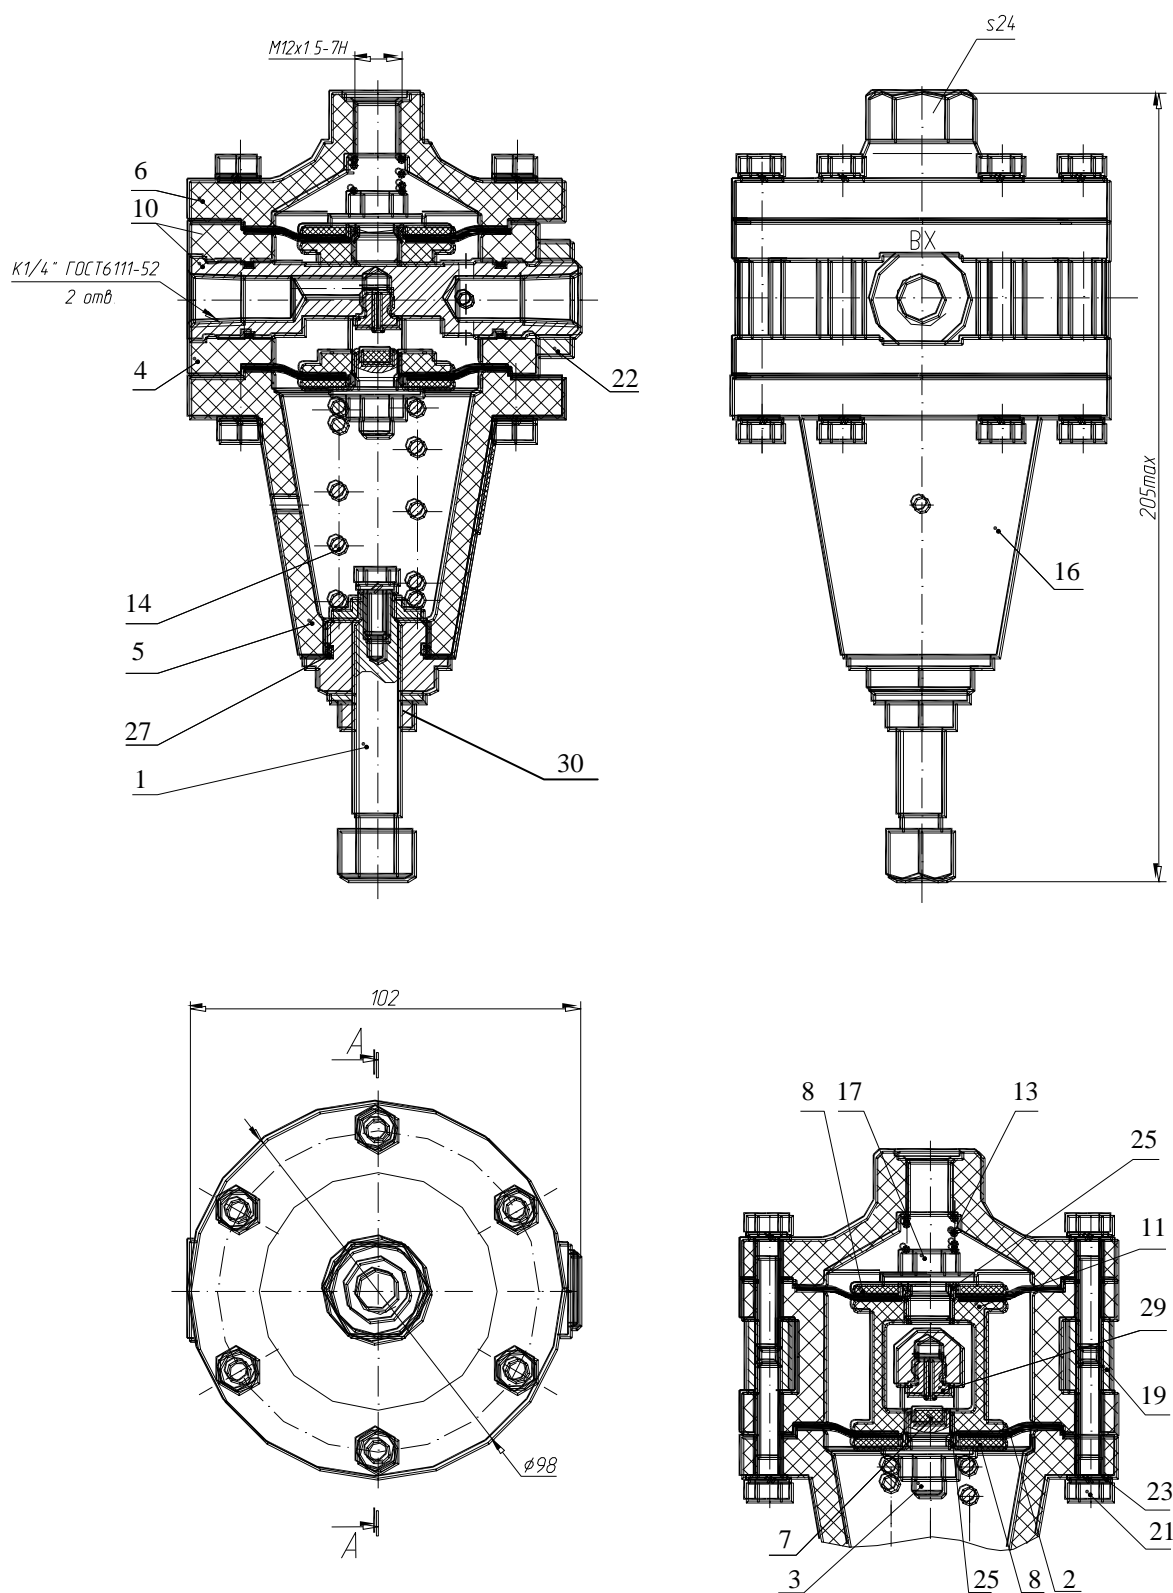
Сборочный чертеж регулятора РДС-ДС-05
